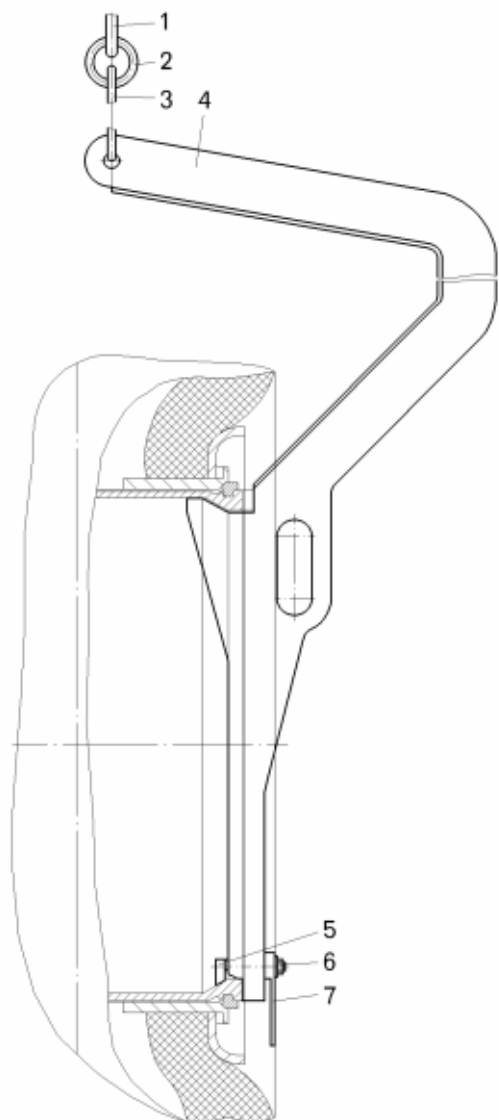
Чалочное приспособление для установки передних и задних внутренних колес:
